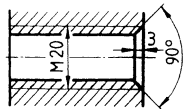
Gewindesenkung dargestellt und bemaßt
